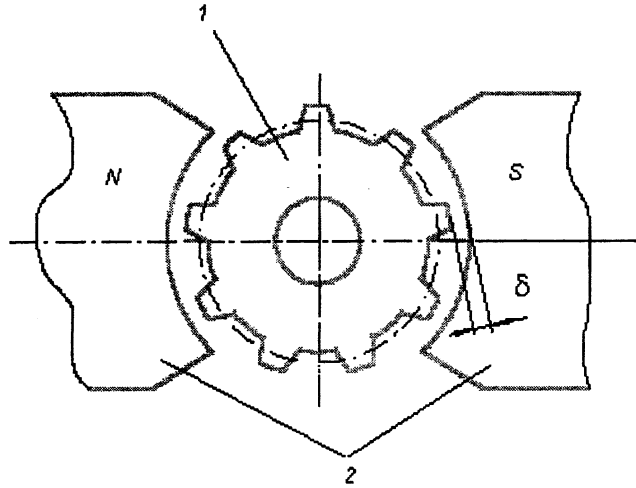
Схема магнитно-абразивной обработки зубчатых колес.
